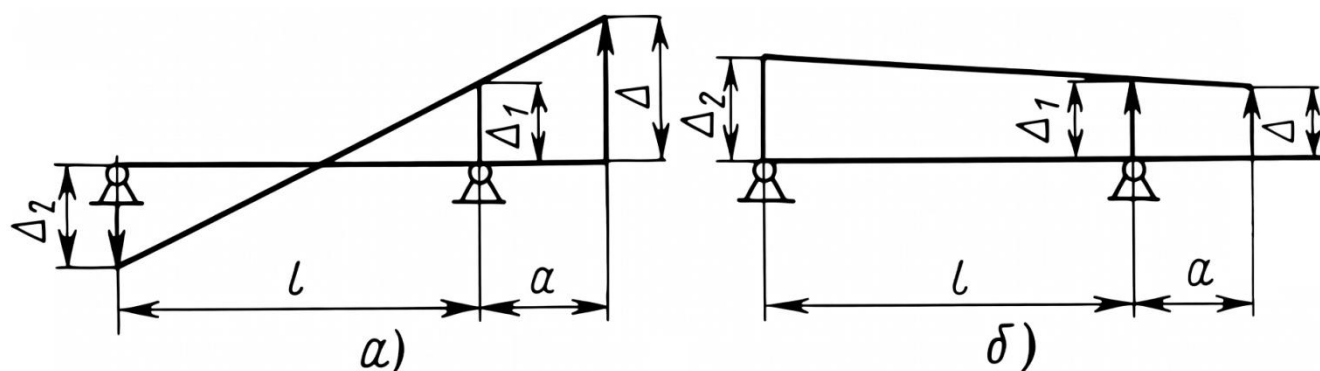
Расположение мест с наибольшим радиальным биением внутренних колец подшипников двухопорного шпинделя в одной плоскости и направленных:
